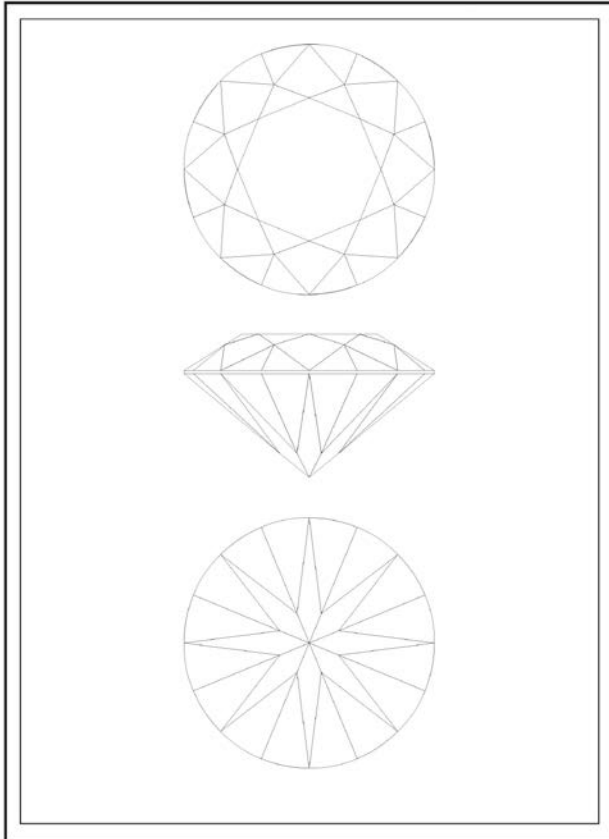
Technisches Zeichnen – Schmuckdiamantschleifer – 8-fach Brillant © Schäfer
